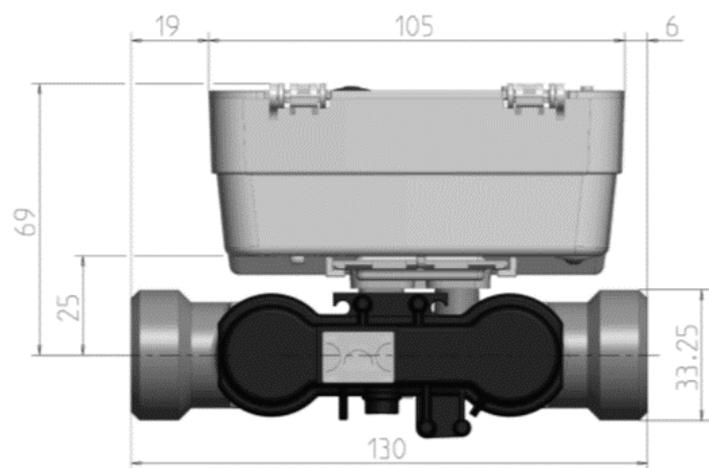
Übersicht Maße Baulänge 130 mm (Gewinde)
